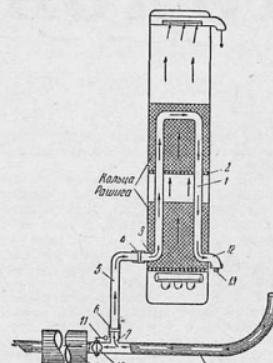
Схема приспособления для подогрева вертикального тонкого очистителя отработавшими выхлопными газами двигателя
